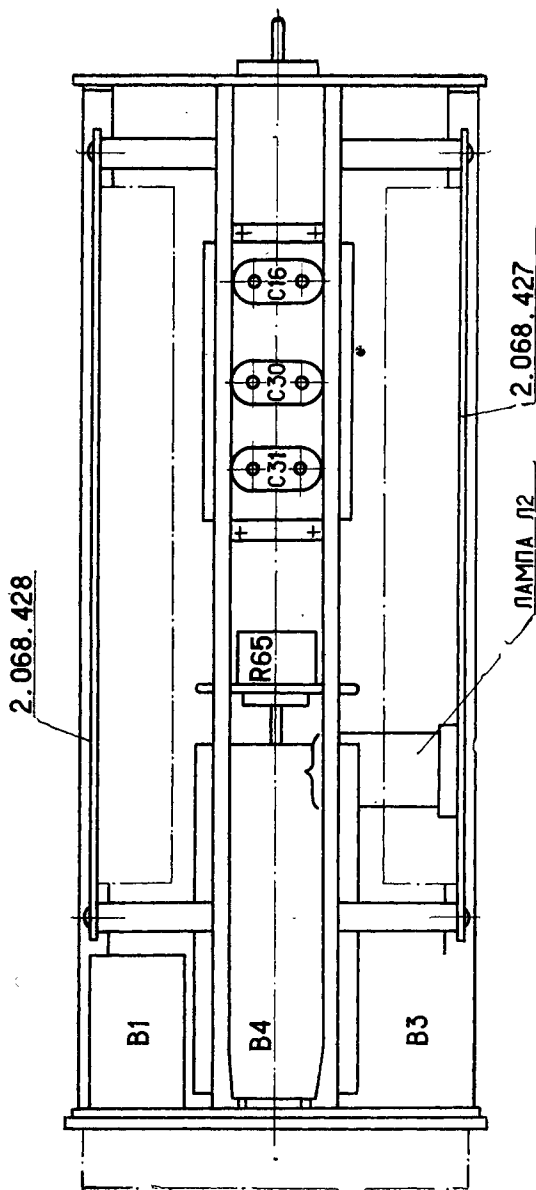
Схема расположения установочных элементов блока развертки (вид сверху)
